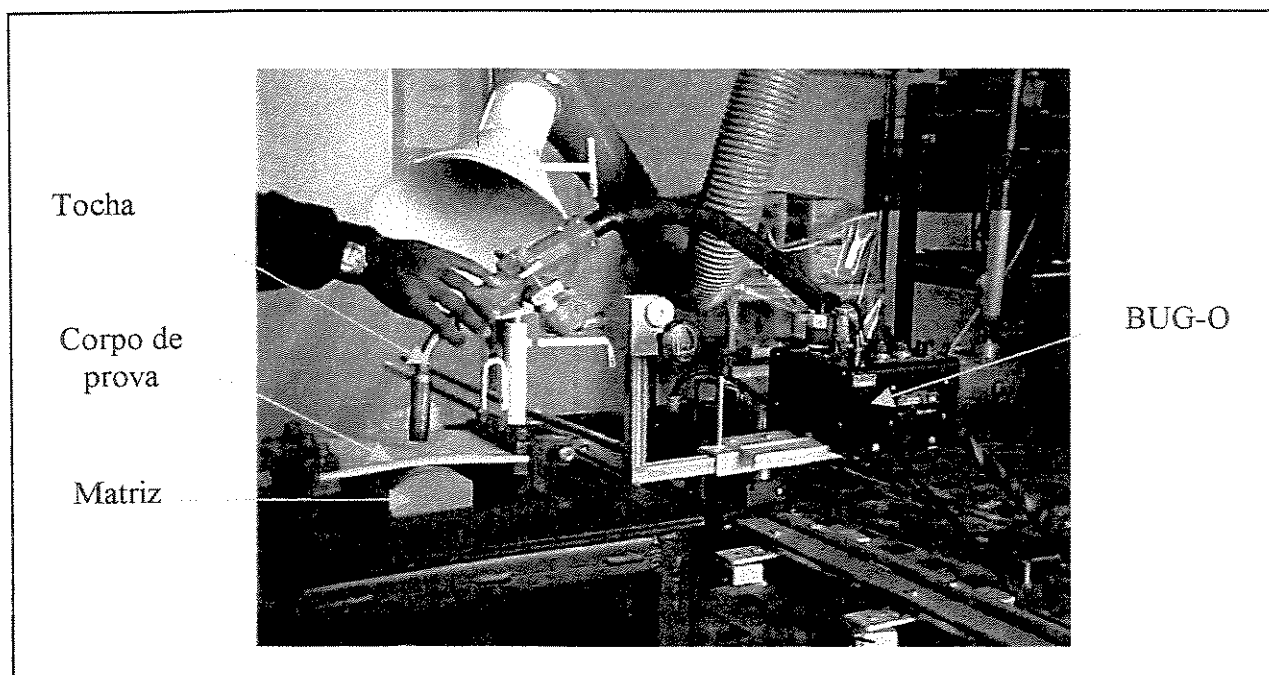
Sistema eletromecânico “BUG-O”, que garante a regulação e controle da velocidade de soldagem e do “stickout” no processo de soldagem FCAW.
